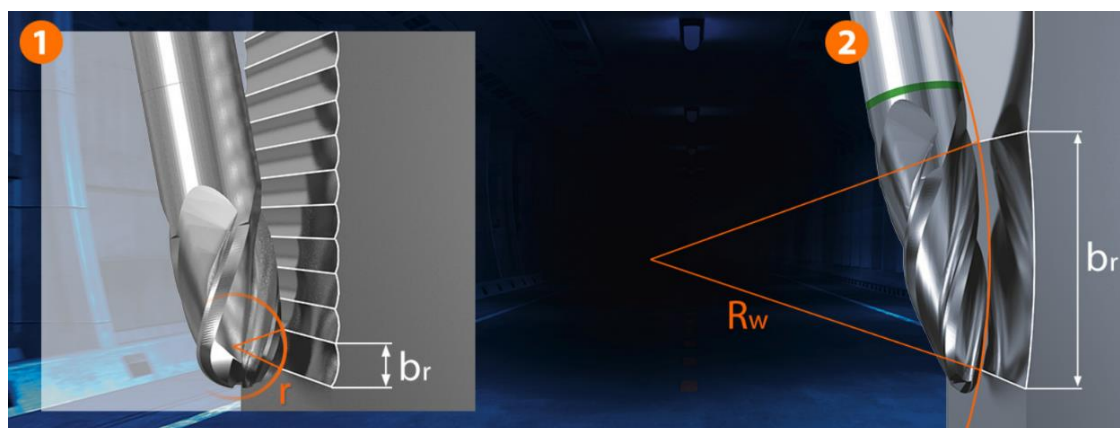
Porovnání kvality povrchu vytvořené kulovou a soudečkovou frézou [28]
